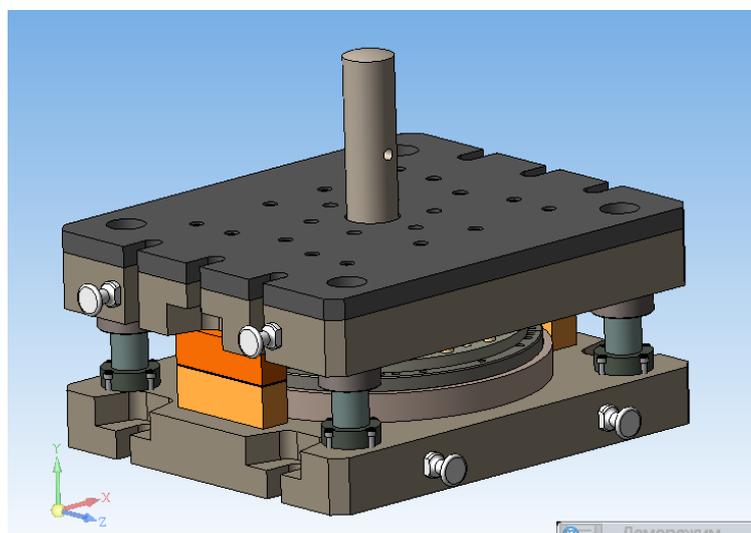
Изометрия штампа совмещенного действия для изготовления детали «Лист ротора крайний»
